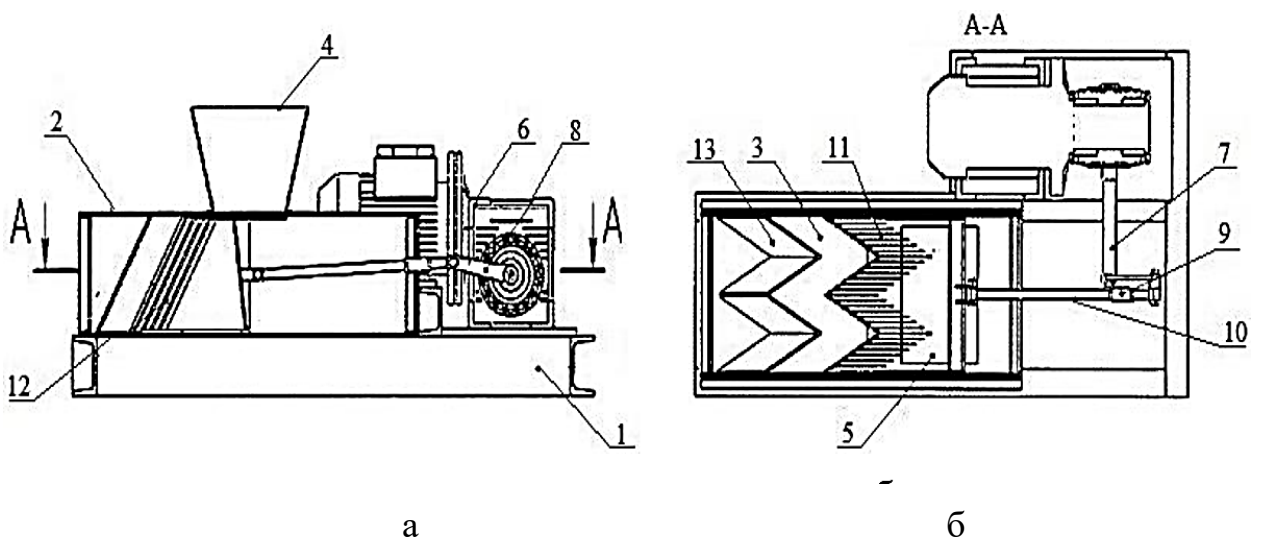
Схема подрібнювача плодоовочевої продукції: а – загальний вигляд, б – вид А-А: 1 – станина, 2 – корпус, 3 – камера подрібнення, 4 – завантажувальна горловина, 5 вивантажне вікно, 6 - мотор-редуктор, 7 - приводний вал, 8 - кривошип, 9 - регулювальна гайка, 10 - шатун, 11 - ножі, 12 - ножова стінка 13 - протиріжучий підпір
